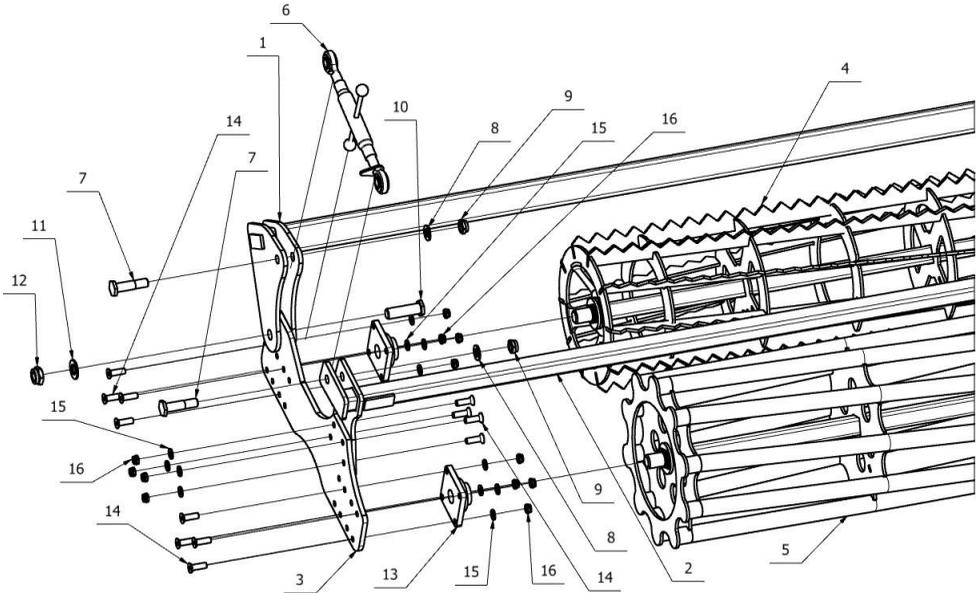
Tandem-Rohrwalze (Ø500mm) - Krümelwalze (Ø420mm)
